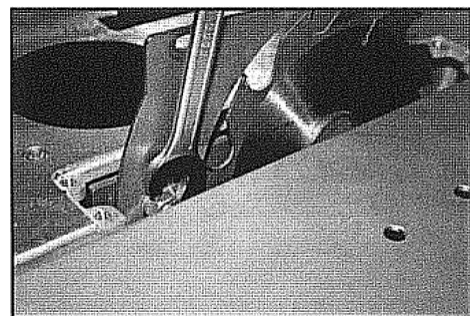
Abstand des Trennmessers zum Sägeblatt einstellen
